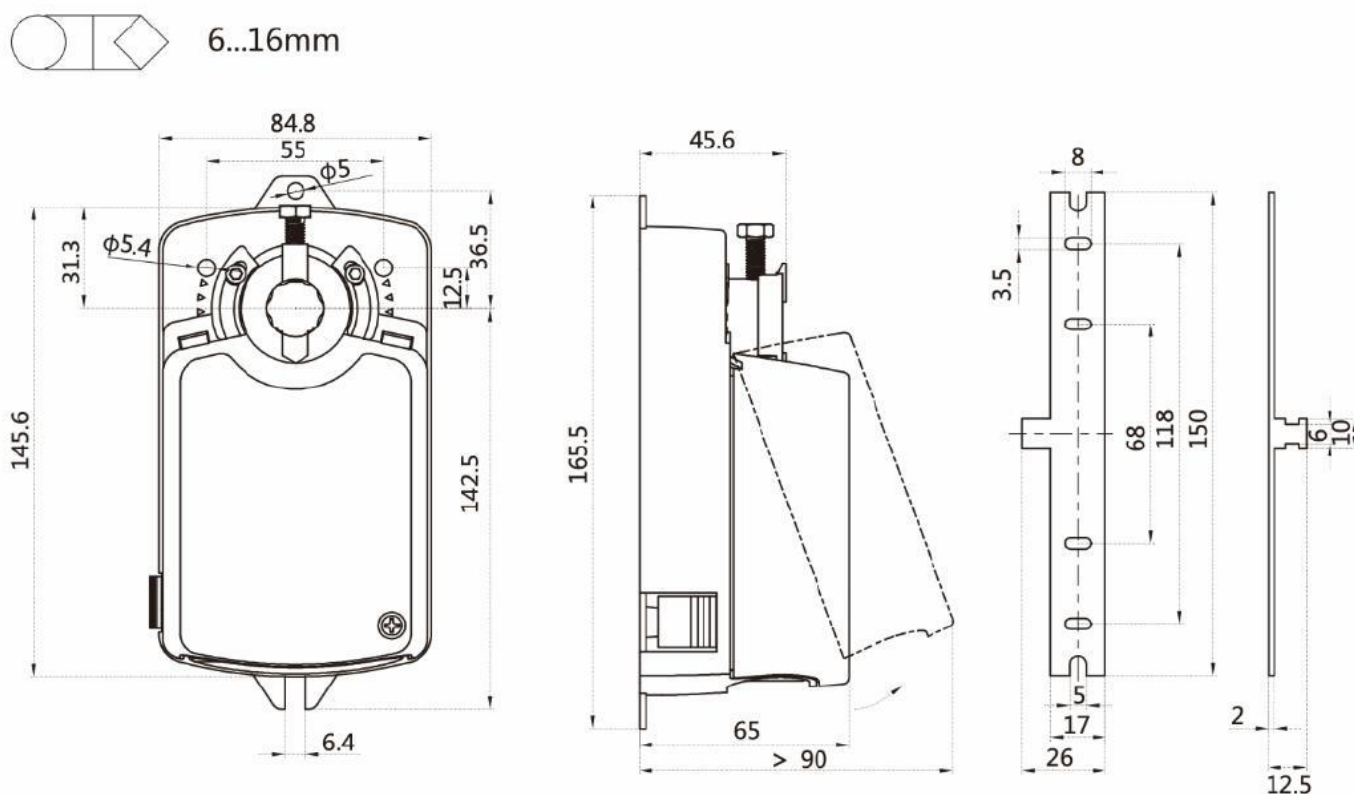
Общий вид и габаритные размеры электропривода VR4RS24-A
